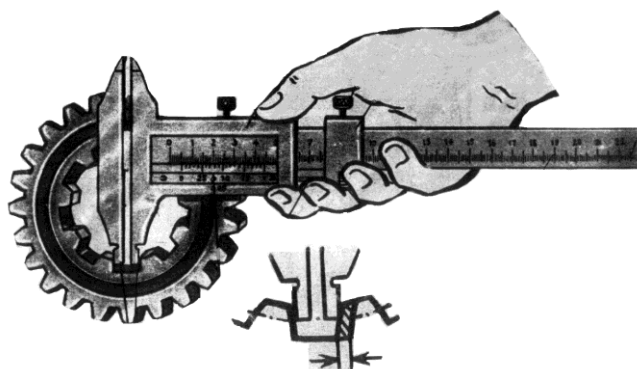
Схема измерения ширины паза ступицы штангенциркулем.
